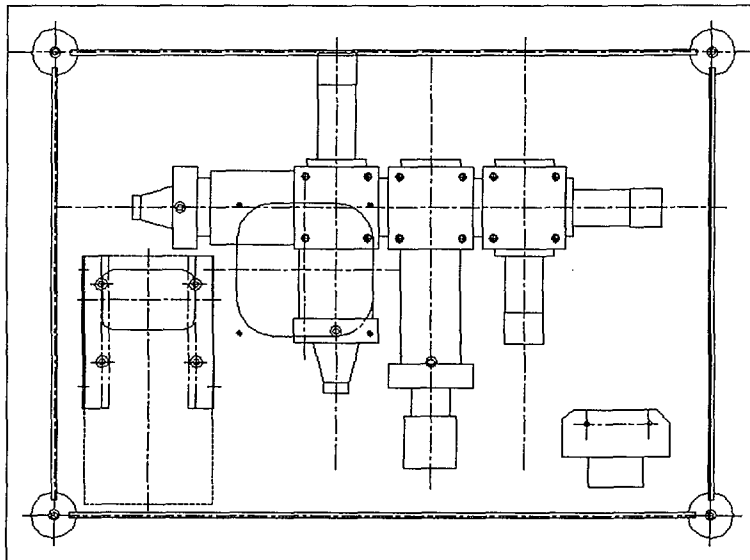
감시장치 평면도 (Layout of Monitoring System)
